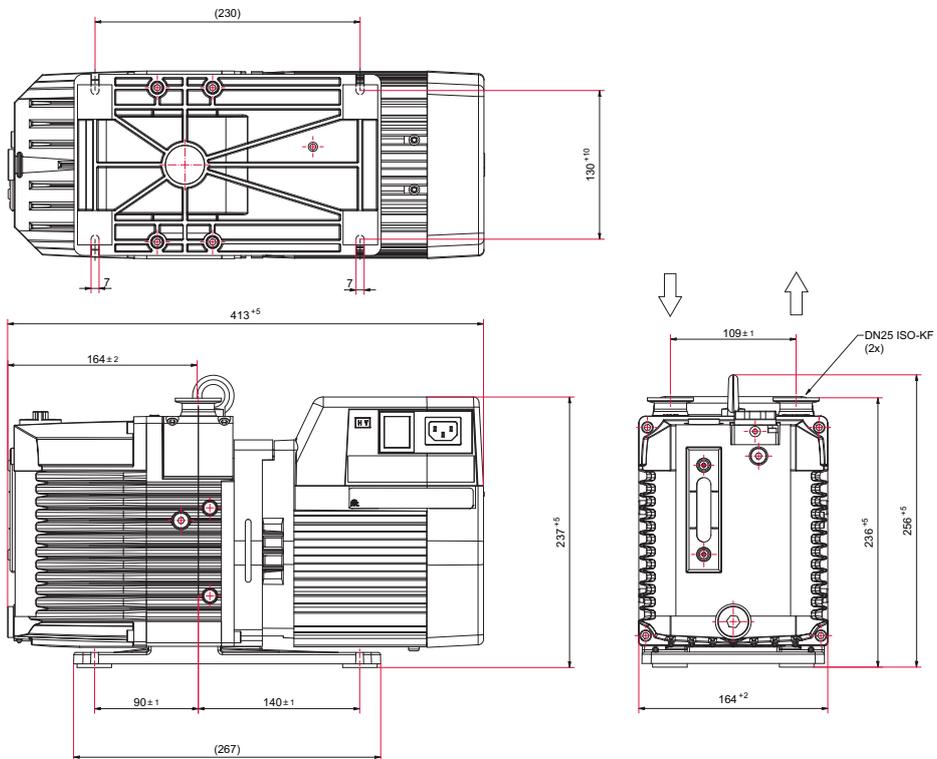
Abmessungen DuoVane 6 mit Einphasenmotor
